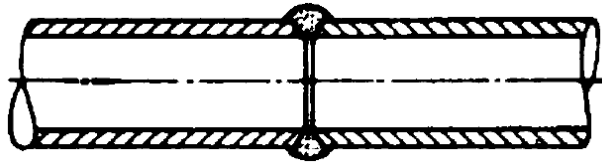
18. Junta por soldadura en tuberías de acero
